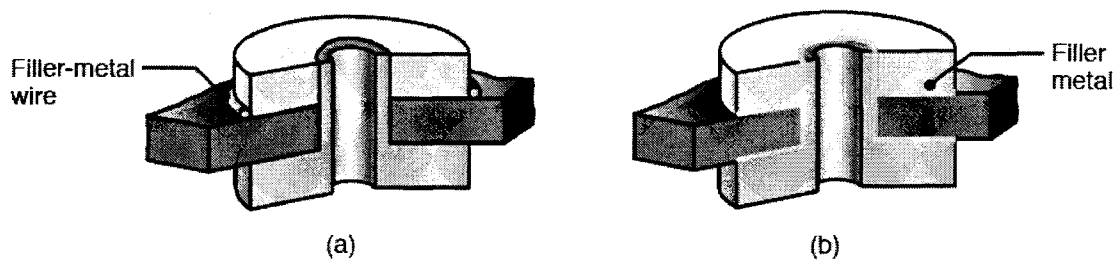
Aplicación en un horno de soldadura. (a) antes y (b) después. Note que el aporte tiene forma de hilo.
